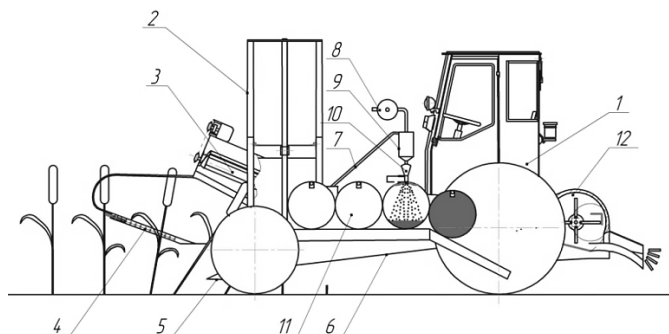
Схема навесного соргоуборочного комбайна со сменными зерновыми бункерами и пневматической системой транспортировки зерна
